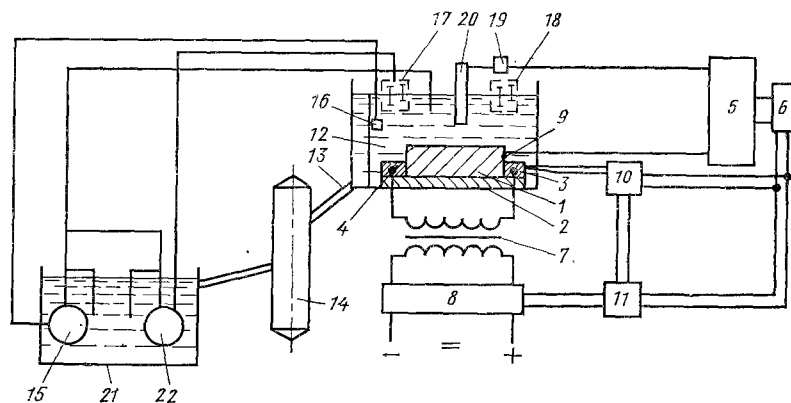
Принципиальная схема станка для электроэрозионной обработки деталей в предварительно нагретом состоянии
